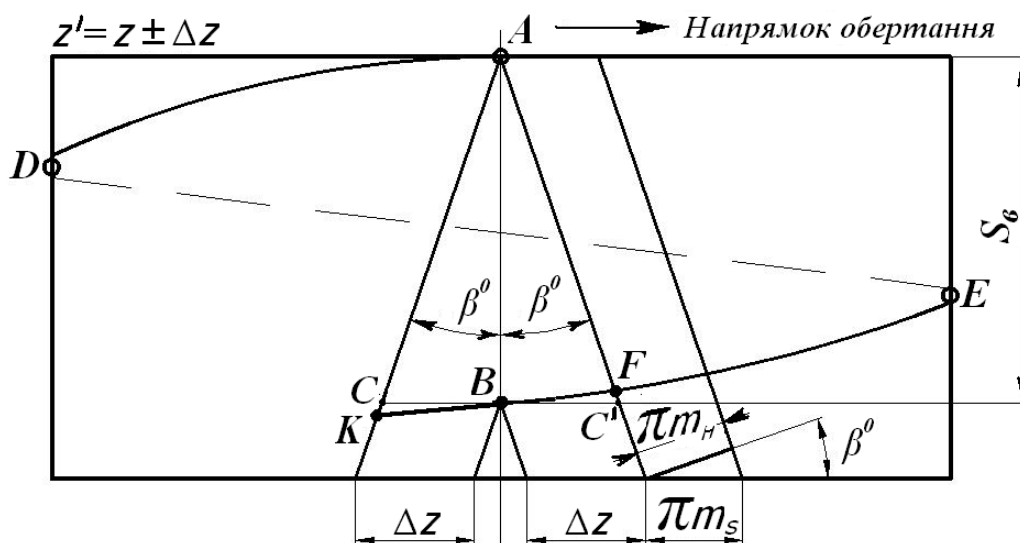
Схема визначення додаткових зубів на витку заготовки
